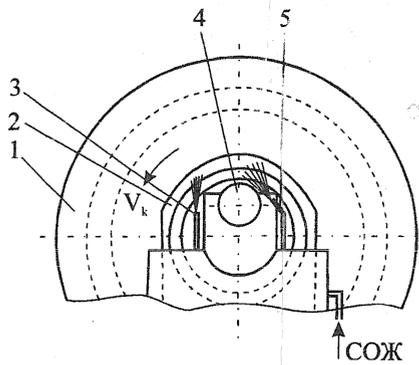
Схема экспериментальной установки на базе станка «Алмаз-6М»: 1 - кожух, 2 - АКВР, 3 - сопло для очистки режущей кромки, 4 - заготовка, сопло для подачи СОЖ в зону обработки
